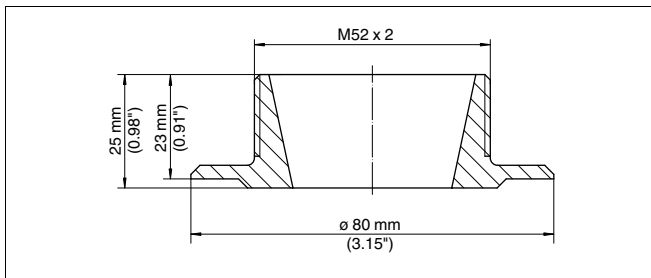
Medidas racor soldado conexión cónica M52 x 2
